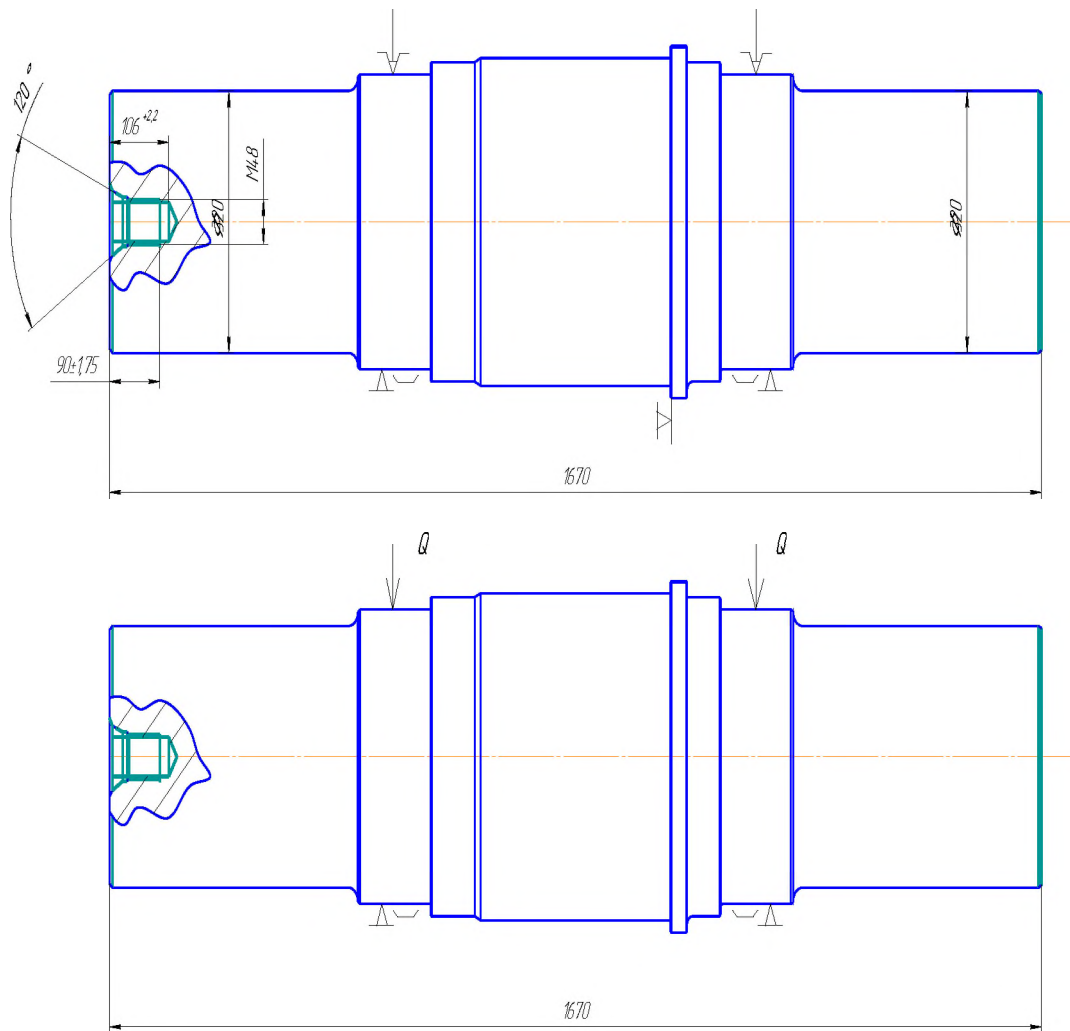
Ескіз механічної обробки деталі вал
